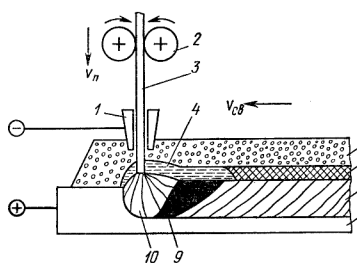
Схема автоматичного дугового зварювання під шаром флюсу
